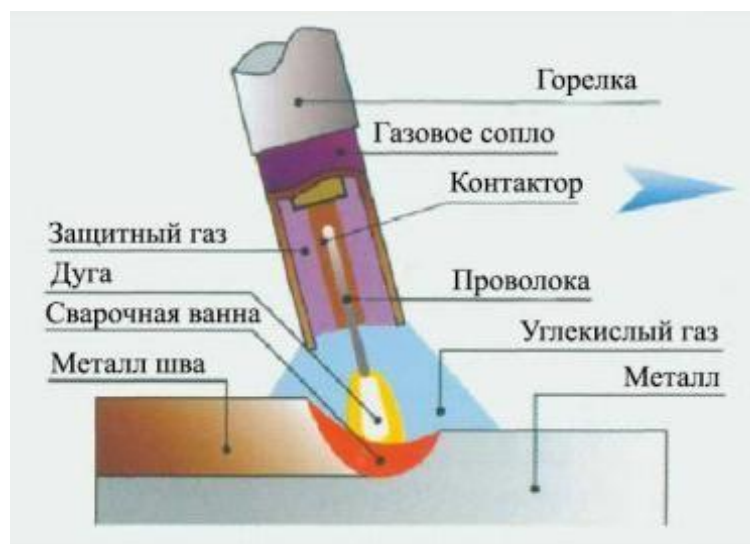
Схема полуавтоматической сварки в углекислом газе [21]
